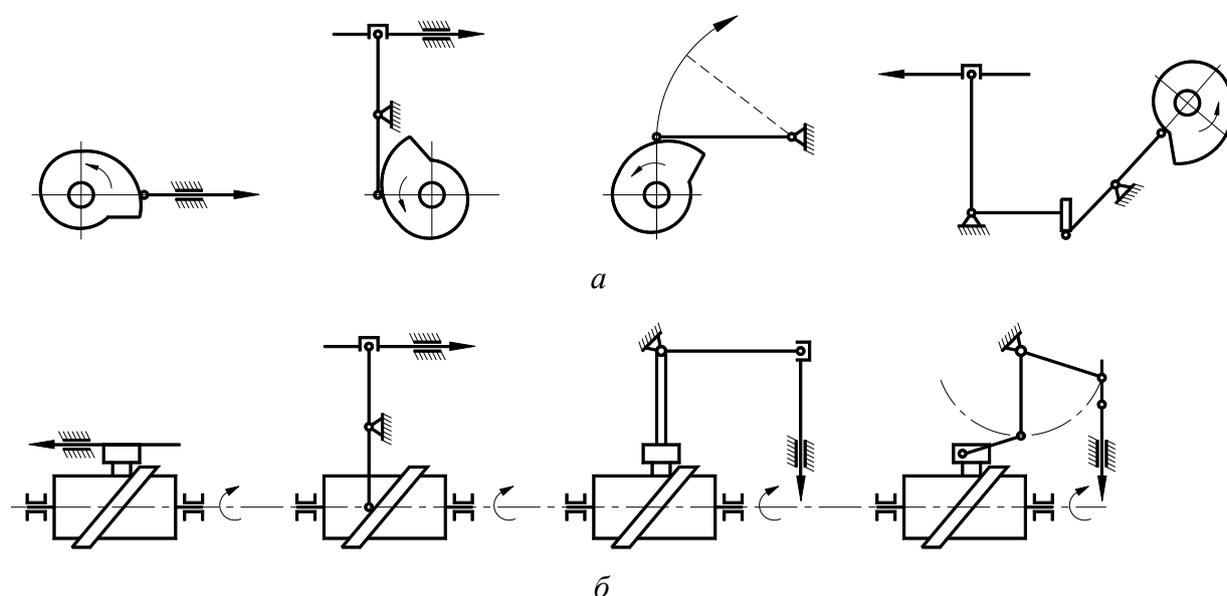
Схемы рычажных механизмов для передачи движений:
